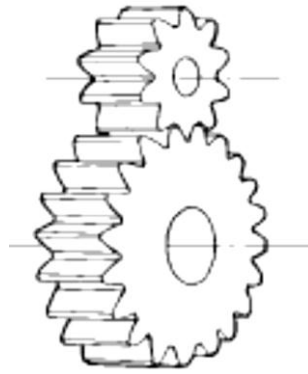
Engrenagem de eixos paralelos de dentado reto [2].
